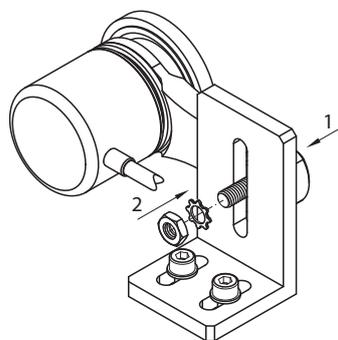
Befestigungsschraube am Montagewinkel befestigen
